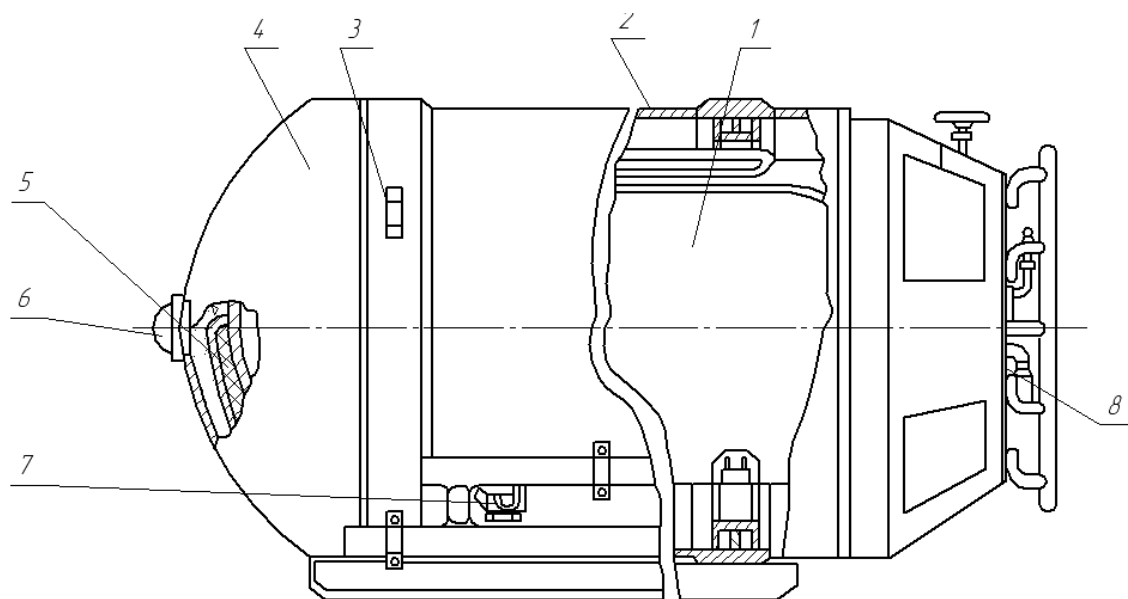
Схема резервуара ТРЖК-7М (вид сверху):
